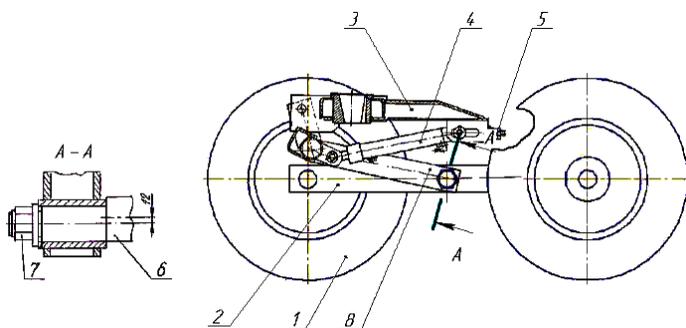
Ходовая система: 1 – колесо с шиной; 2 – балансир; 3 – опора ротора; 4 – гидроцилиндр; 5 – гайка регулировочная; 6 – цапфа эксцентриковая; 7 – гайка цапфы; 8 – балка балансиров
